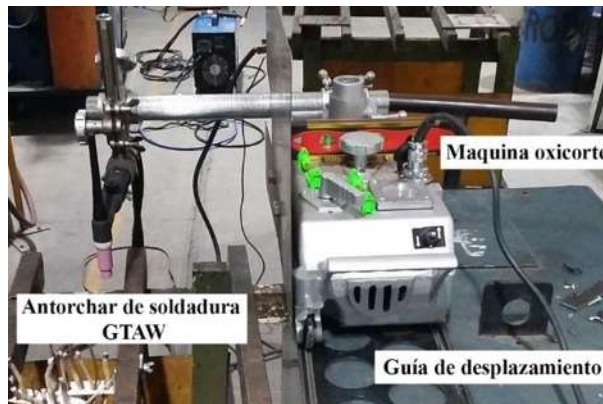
Proceso de soldadura GTAW semiautomático mediante máquina oxicorte portátil Harris Super.
